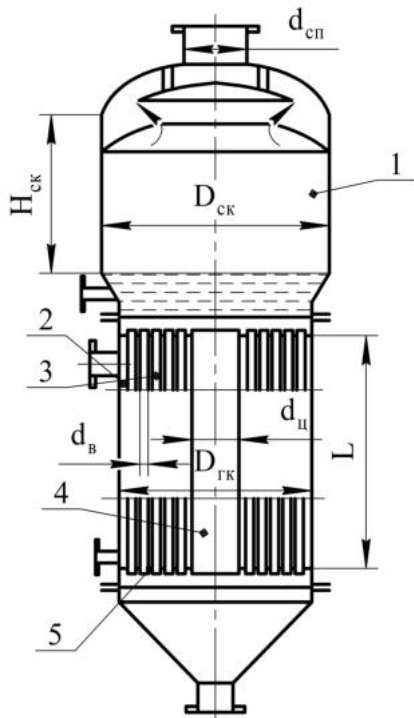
Основні конструктивні розміри випарного апарата: 1 – сепараційна камера; 2 – грійоча камера; 3 – кип’ятильні труби; 4 – центральна циркуляційна труба; 5 – трубна решітка
